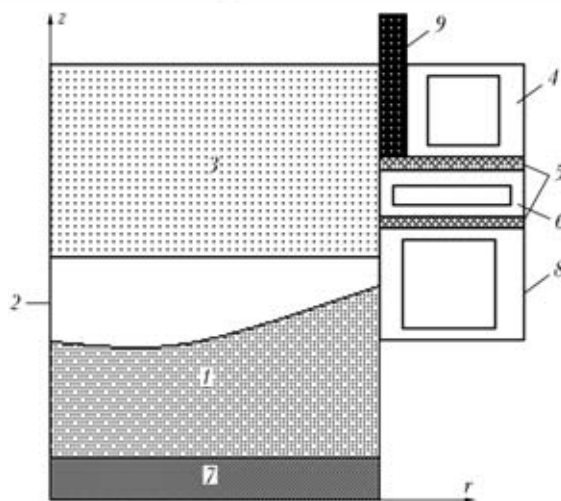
Схема плавки ЭШП в токоведущем кристаллизаторе: 1 — слиток; 2 — металлическая ванна; 3 — шлак; 4 — токоведущий кристаллизатор под напряжением U ; 5 — изолятор; 6 — кристаллизатор шунтирующий шлаковую ванну; 7 — поддон; 8 — кристаллизатор; 9 — графитовая футеровка
